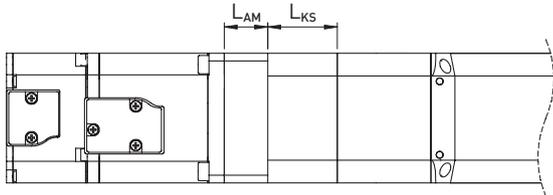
Motoranbindung Linearmodule HM-S ohne Riementrieb
